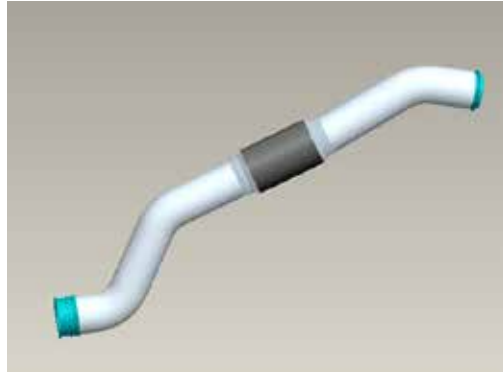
Sólido del bajante de escape realizado en Pro/ENGINEER.
